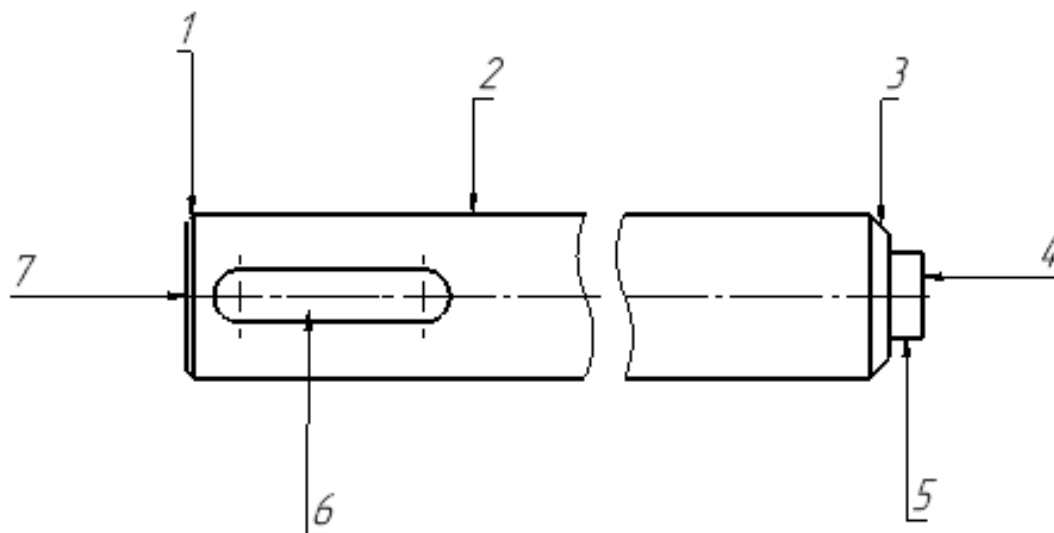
Схема позначення оброблюваних поверхонь:
